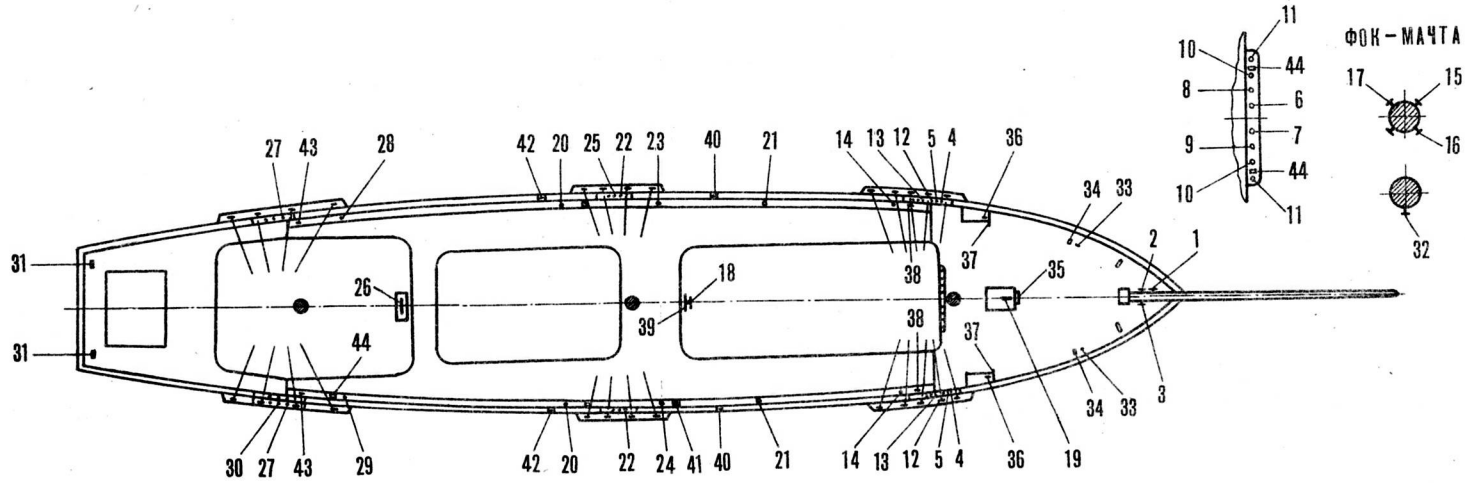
План крепления снастей трехмачтовой бермудской шхуны
